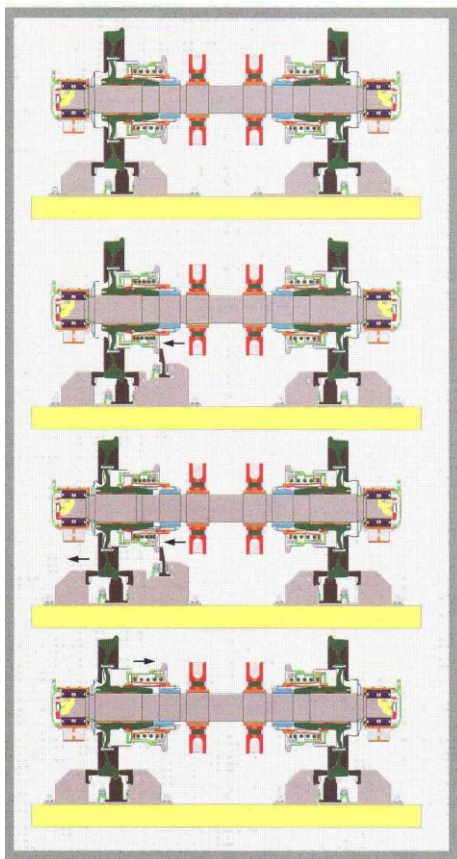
Схема колесной пары с подвижно закрепленными колесами *SUW-2000
